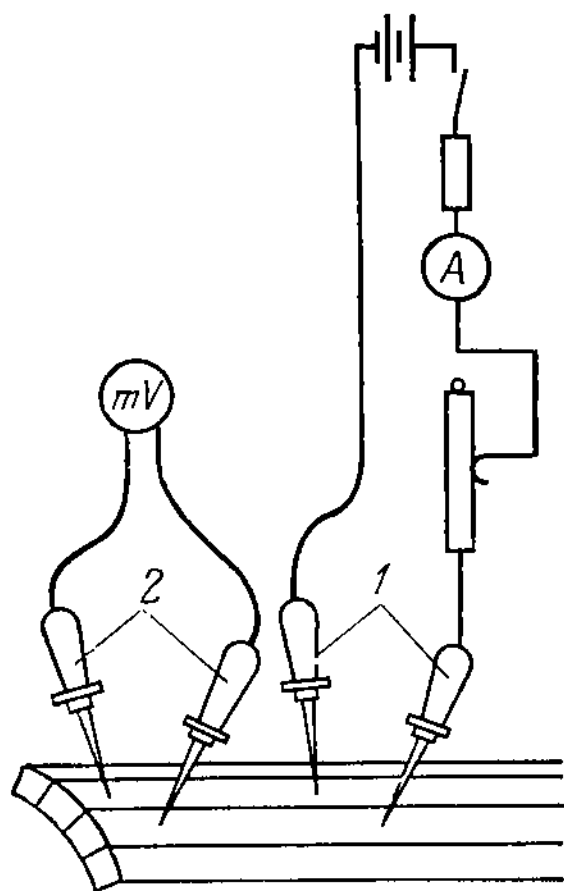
Схема для проверки соединений обмотки якоря машины:
